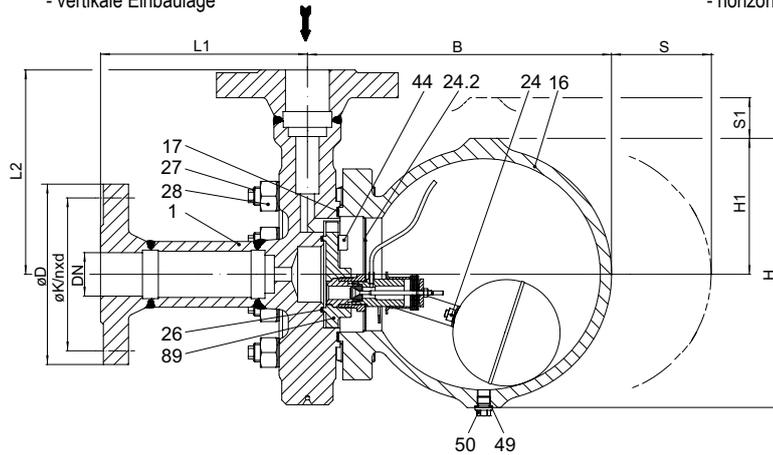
1 ECK-Ausführung mit Flanschen - vertikale Einbaulage
